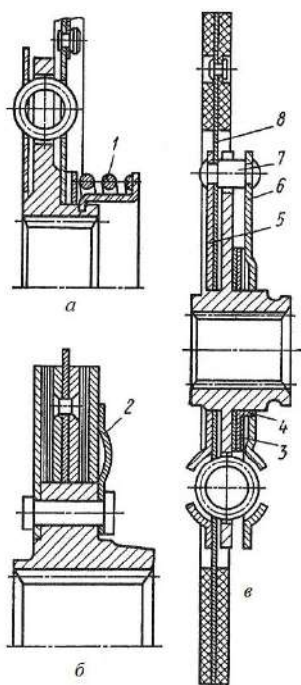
Конструкції демпферів: *а* – автомобіля ГАЗ-24; *б* – фірми «Фіхтель і Сакс»; *в* – ВАЗ 2101; 1 – гвинтова пружина; 2 – пластинчаста пружина; 3 – тарілчаста пружина; 4 – натискний диск; 5, 6 – диски демпфера; 7 – упор; 8 – диск-тримач
